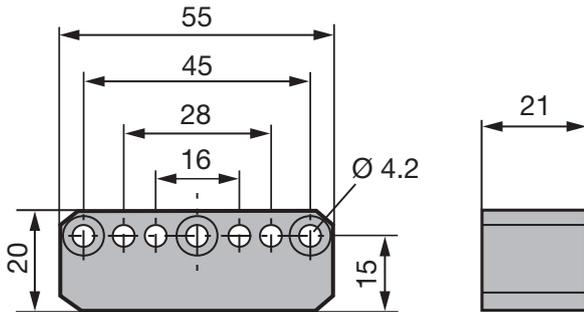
Medidas de montaje del sensor de posición BTL5-P-5500-2
